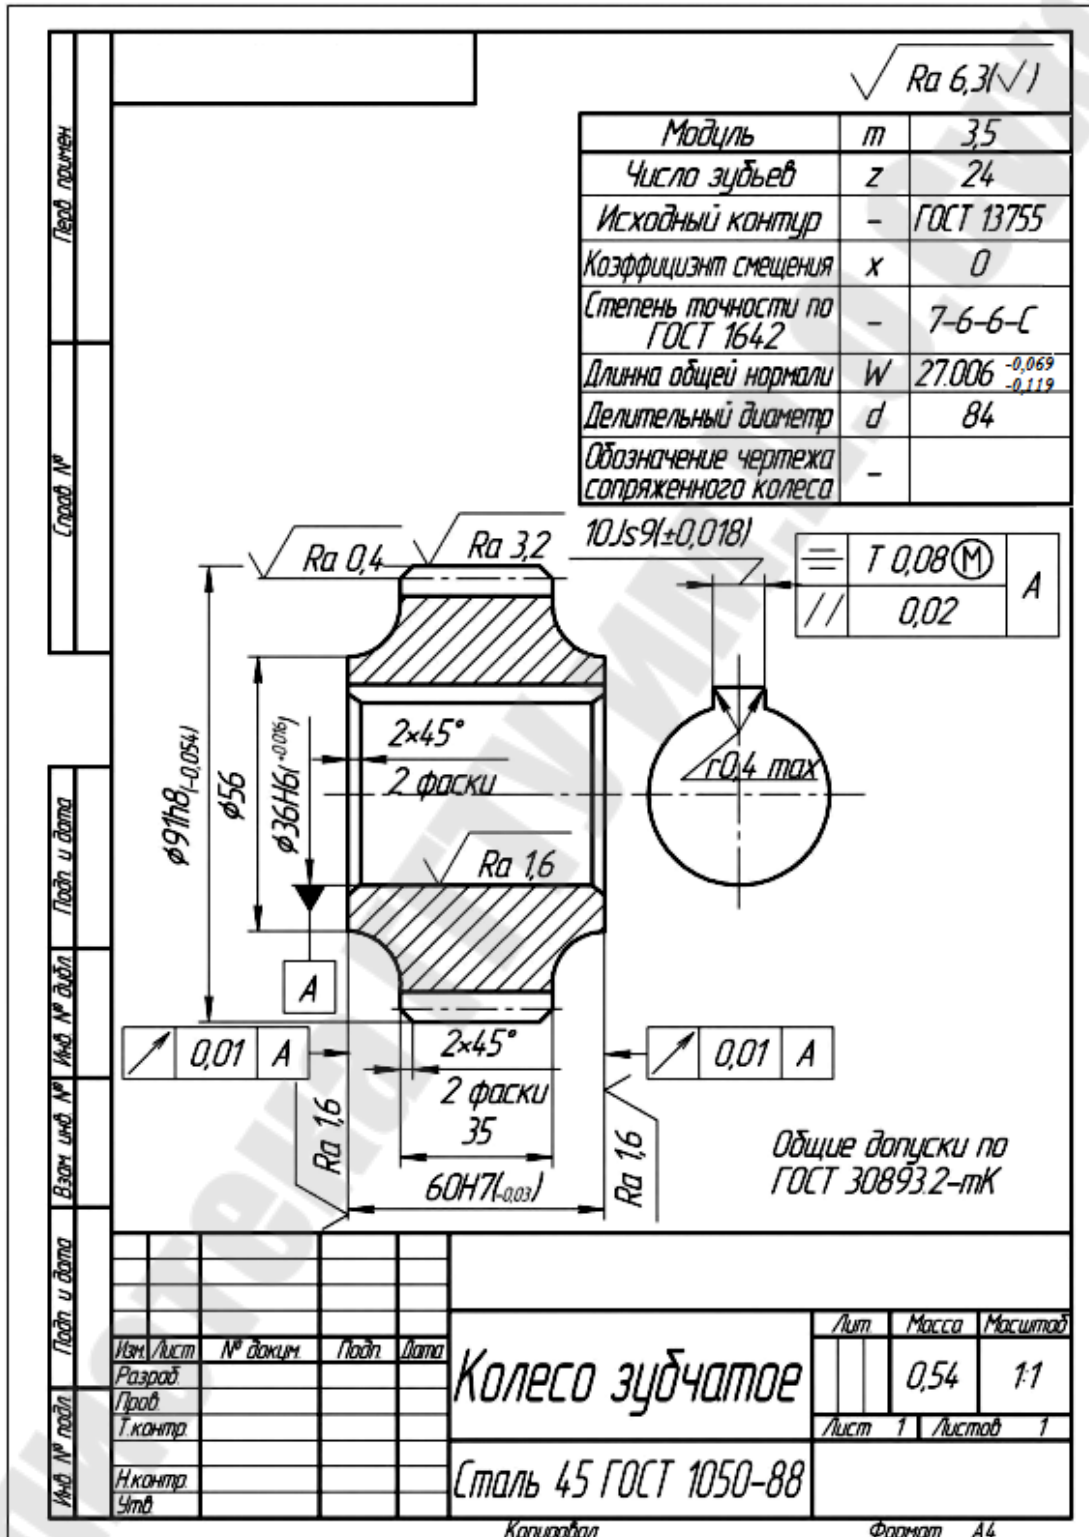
Пример рабочего чертежа зубчатого колеса
